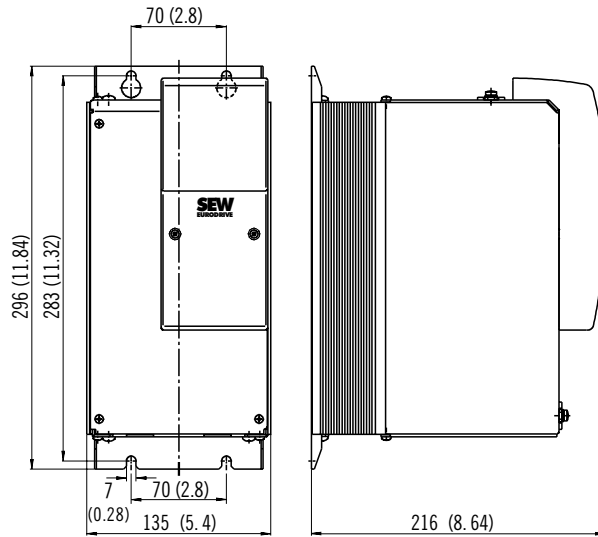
Dimensional para módulo de alimentação buffer FNP 020-503
